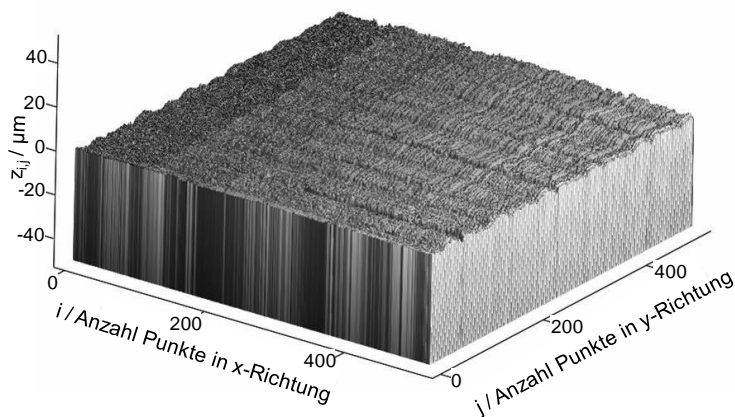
3D Messung einer gefrästen Oberfläche.
